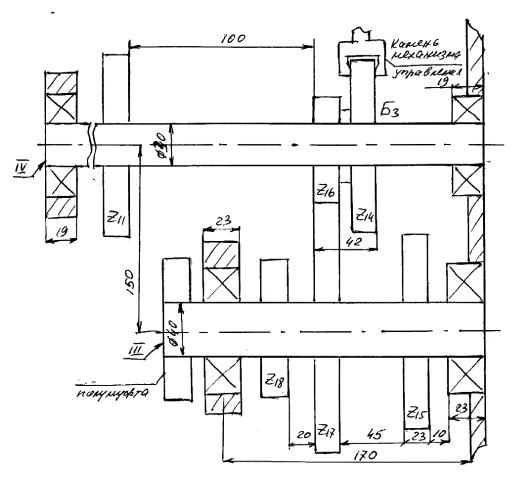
Компоновочная схема развертки наиболее нагруженной группы передач
